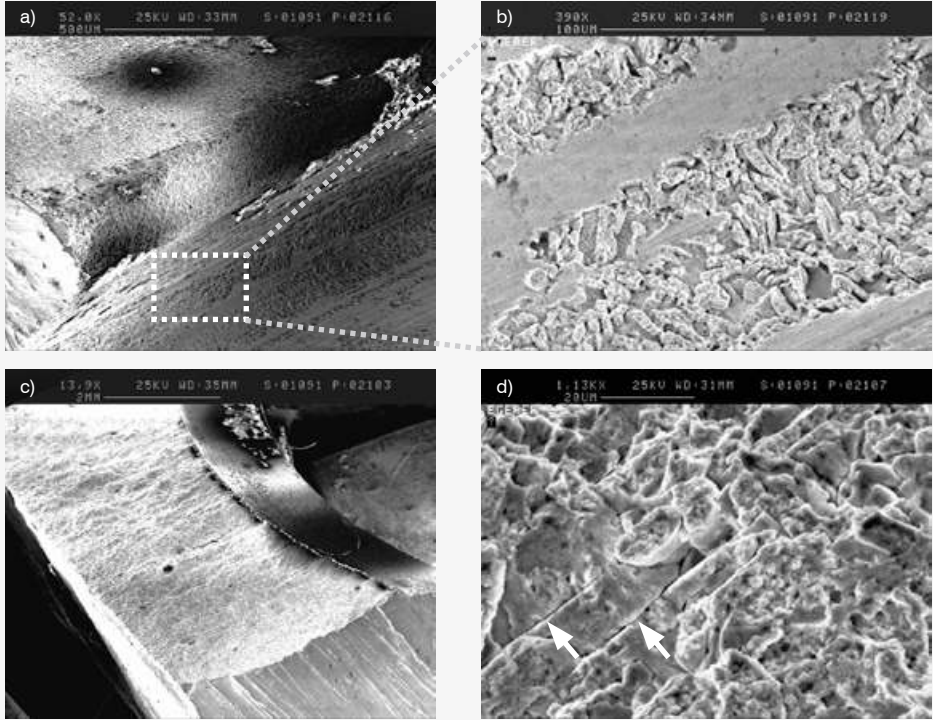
bis d: Vorlaufgewinde im Bereich Einschraubtiefe: a) und b) Risse entlang des Gewindekern-durchmessers; c) und d) Detailaufnahmen
